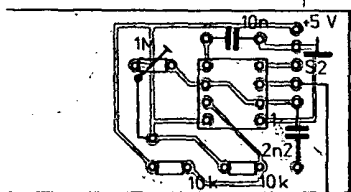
Obrazec plošných spojů desky T123 (strana spojů)
